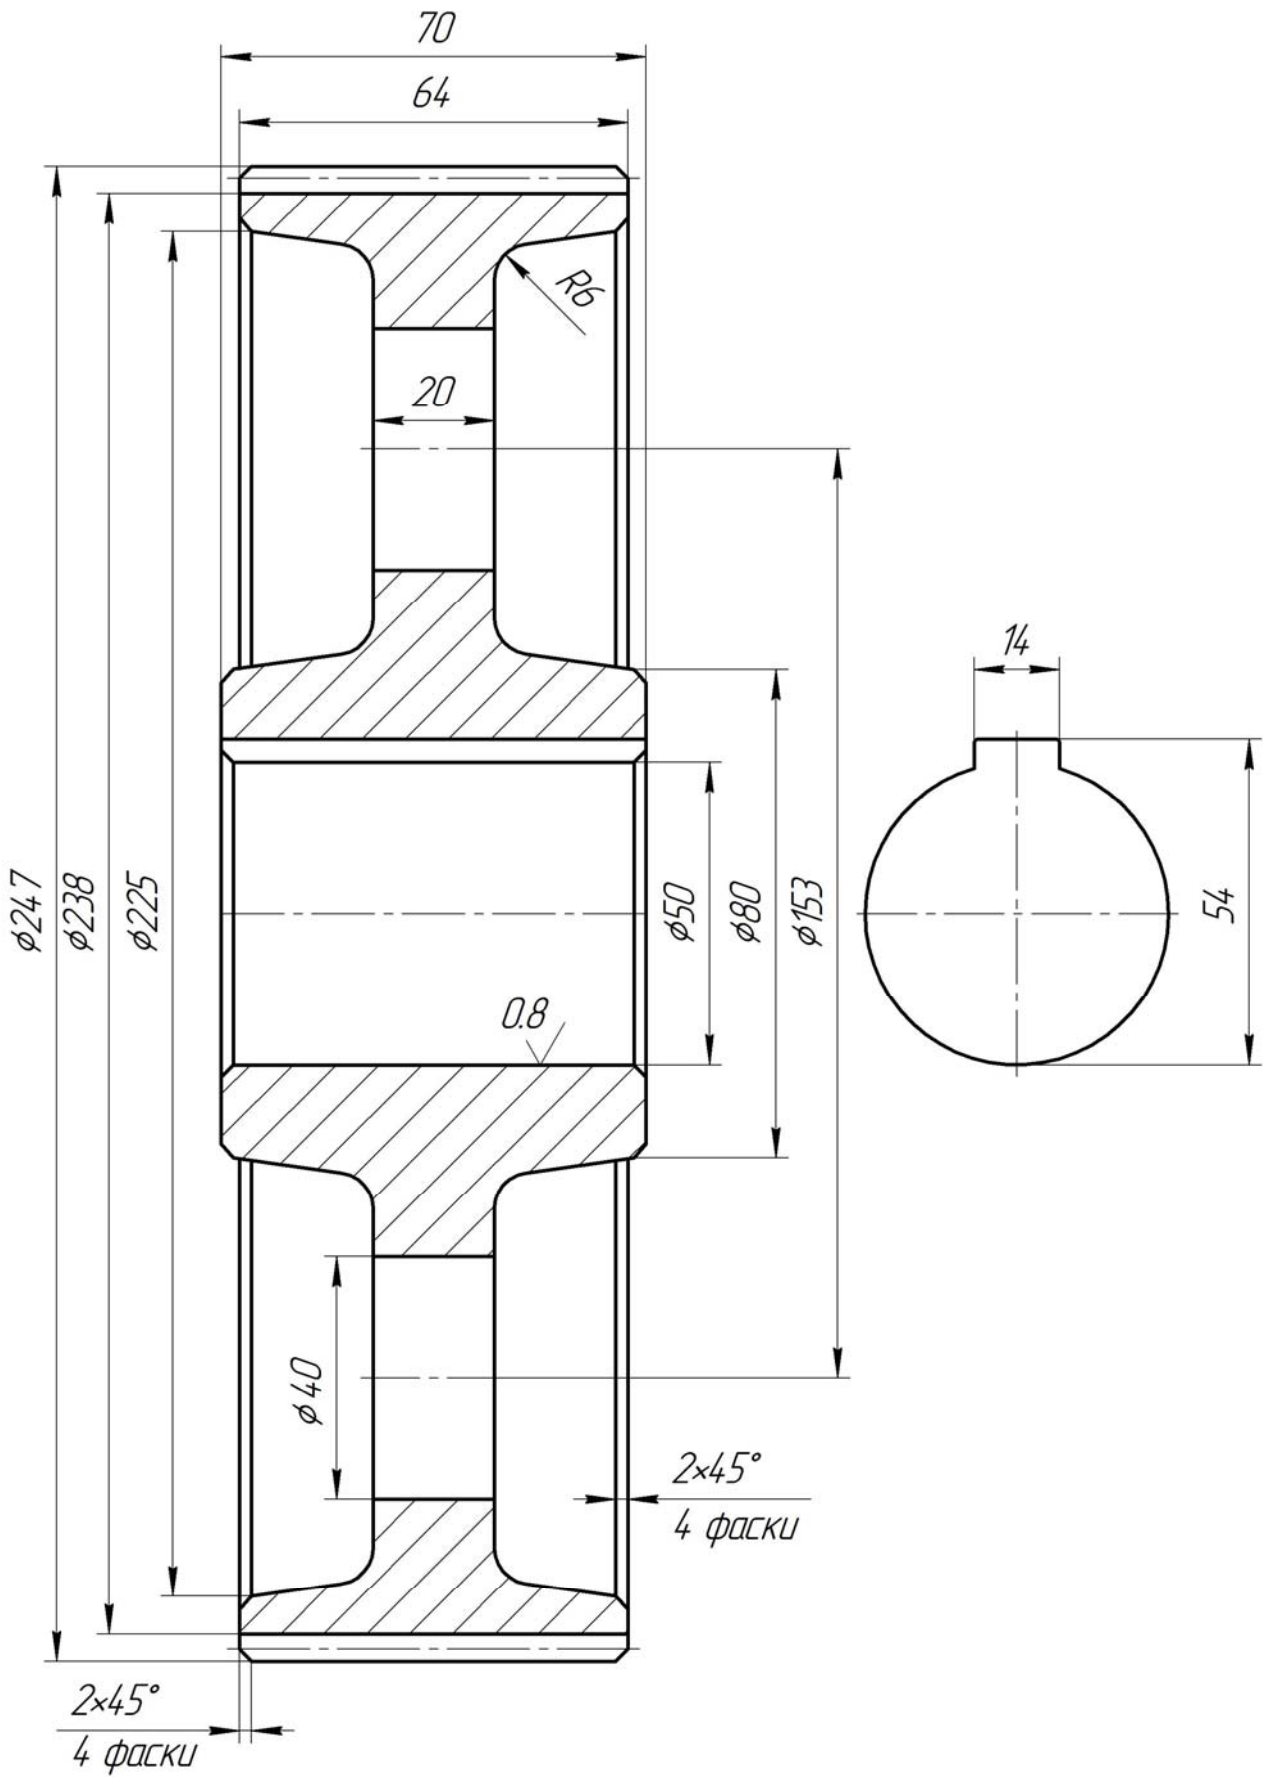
Ескіз циліндричного зубчастого колеса
